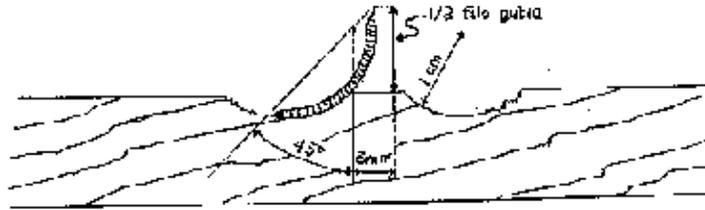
Forma de corte oblicuo para ensayo de torneado.
